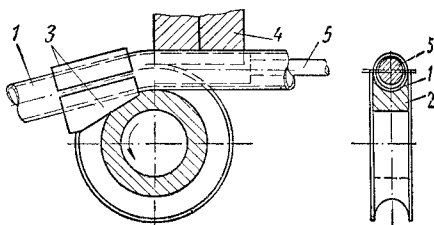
Схема гибки трубы роликом без дорна; 1 — изгибаемая труба; 2 — рабочий сектор с ручьем для размещения изгибаемой трубы; 3 — зажим для закрепления трубы; 4 — прижимной ролик.
